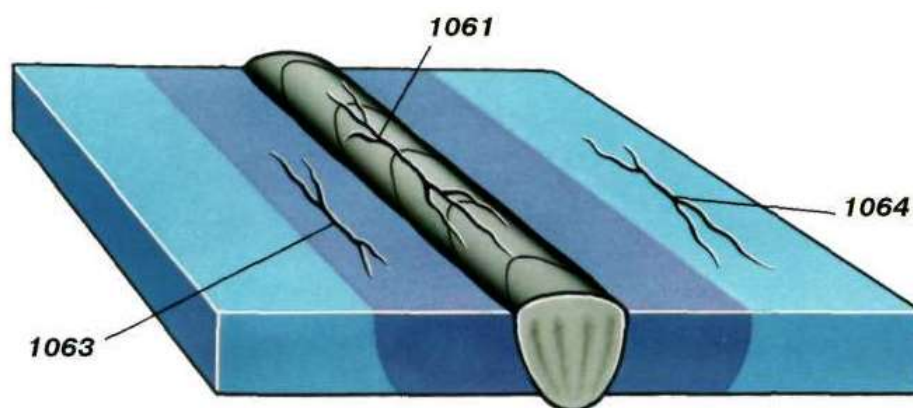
Дефекты сварного шва по типу разветвленных трещин
